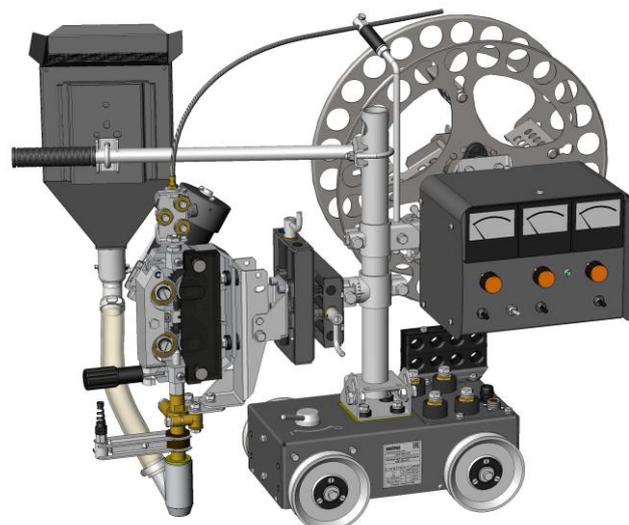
Автомат сварочный АДГ-630 исп.03
